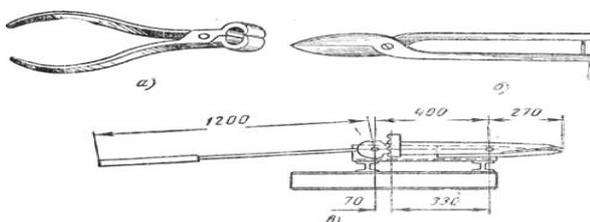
Инструменты для резки металла: а — кусачки, б — стуловые ножницы, в — рычажные ножницы
